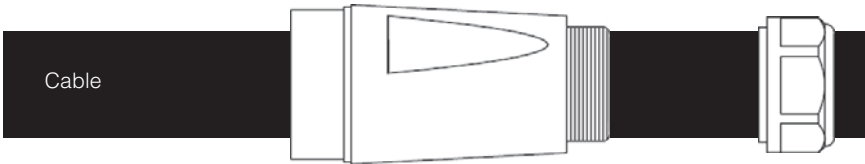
Paso de la tuerca del cable y de la carcasa trasera por el cable
